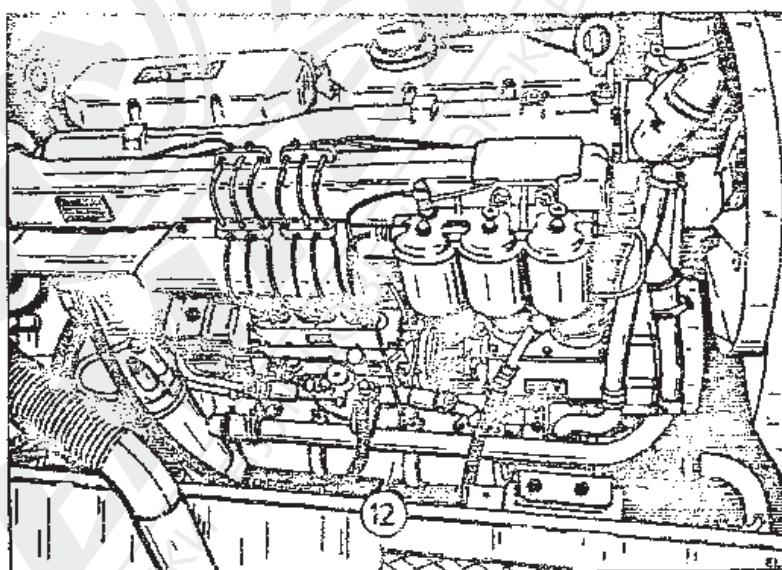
Радиатор смазочного масла двигателя /поз. 12/
